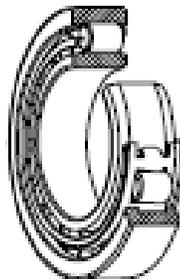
Rodamientos de rodillos cilíndricos
